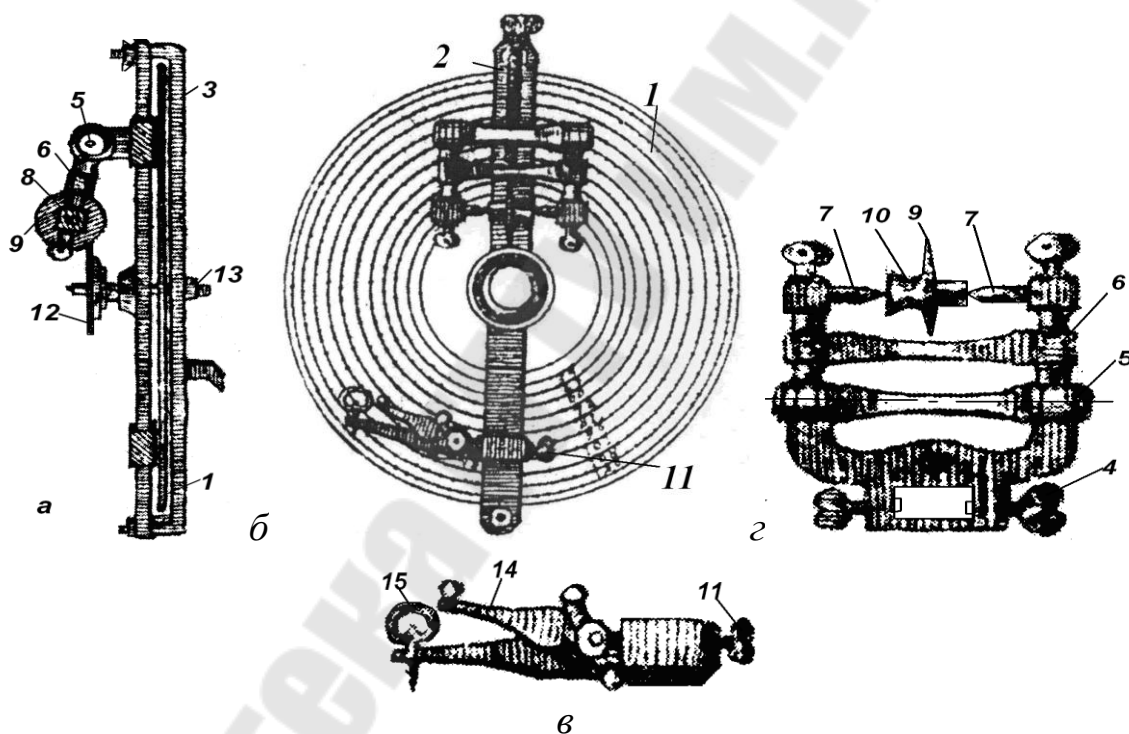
Устройство для фрезерования часовых зубчатых колес. Нач. 18 в. По Н. Биону
